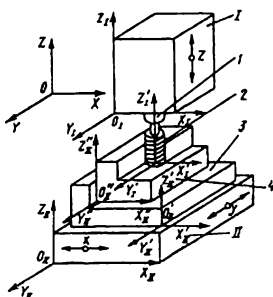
Схема розташування інструмента і деталі при обробці на БВ з вертикальним розташуванням шпинделя
